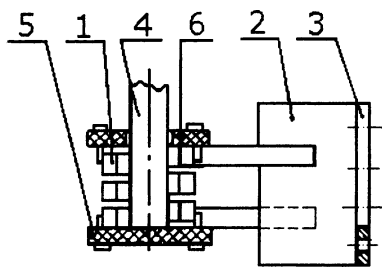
Типовой индуктор для нагрева заготовок под выдавливание: 1 — индукционная катушка; 2 — токоподводящие шины; 3 — колодки крепления к трансформатору; 4 — нагреваемая заготовка; 5 — нижняя плита; 6 — верхнее центрирующее кольцо
